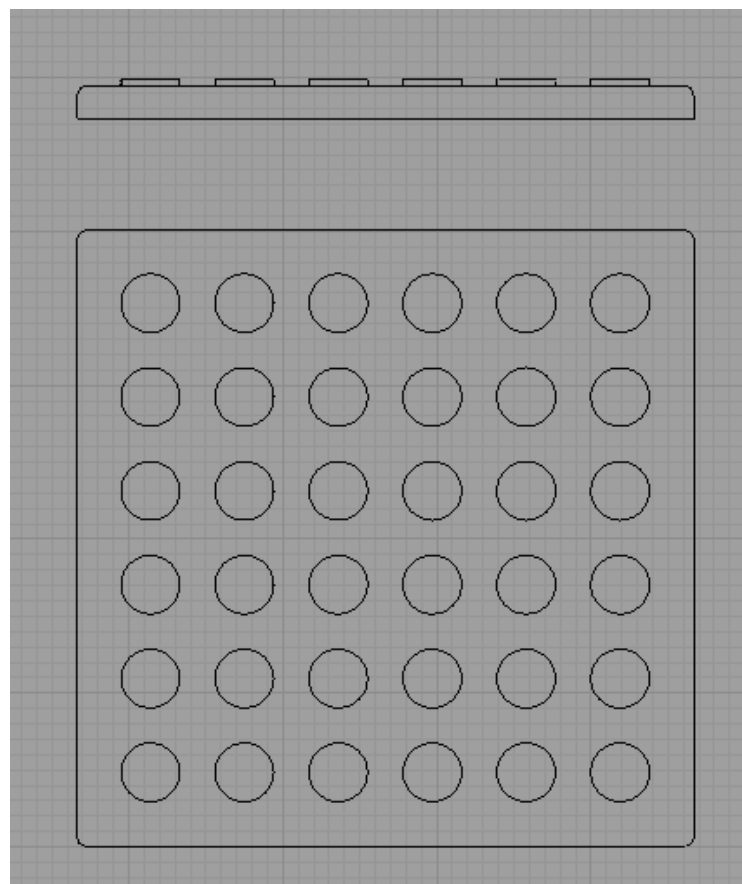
Planimetría Superficie Diseño Accesible. Elaboración propia.
